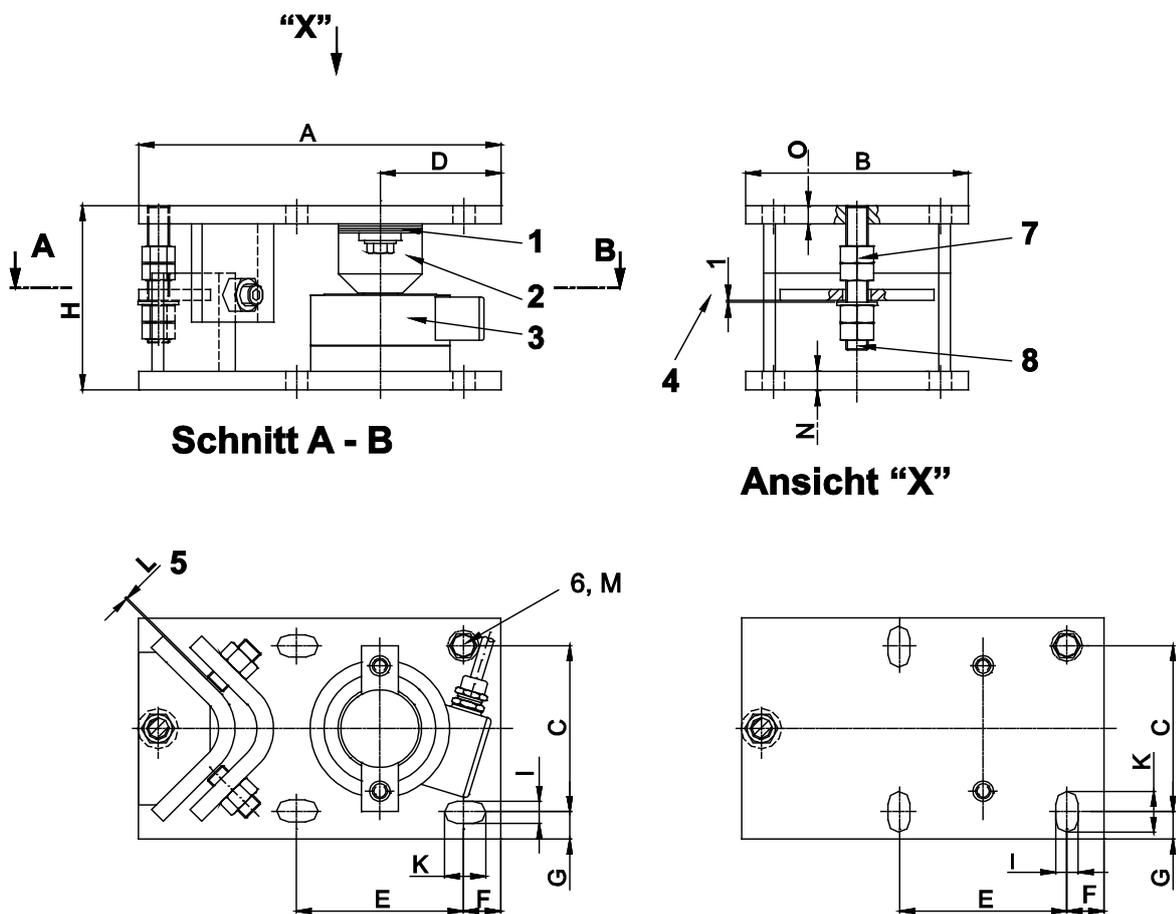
Einbauzeichnung der Kompaktlager DKM 0,25 ... 33 t
